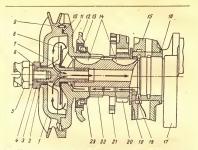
Центробежный маслоочиститель и передний коренной подшипник коленчатого вала двигателя «Запорожец»:
